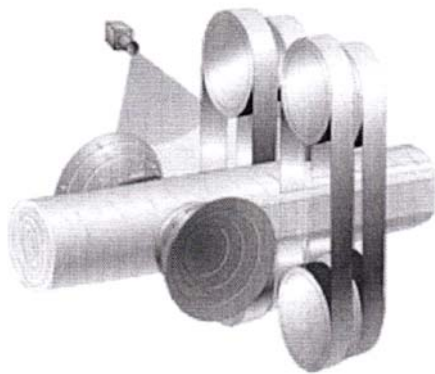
Схема работы ленточнопильного станка с фрезерно-брусующим модулем
